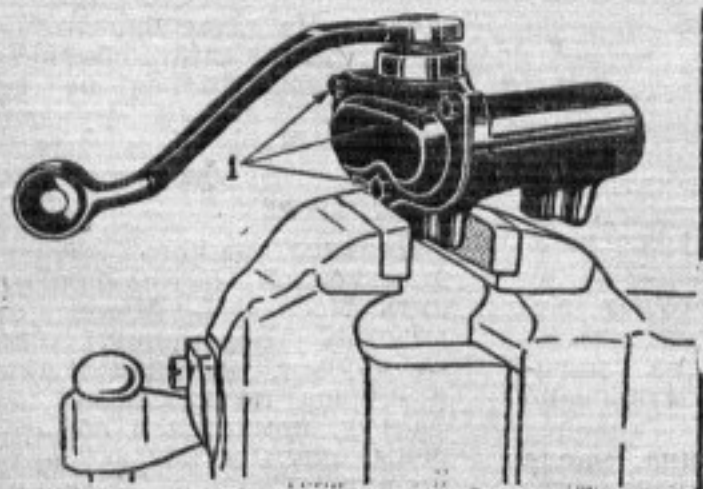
Установка амортизатора в тисках. 1 — болты крышки корпуса
